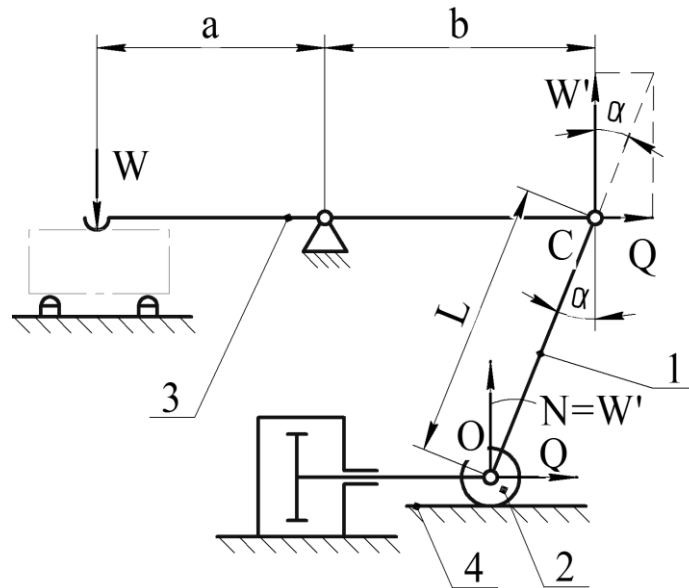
Однорычажный шарнирно-рычажный механизм
